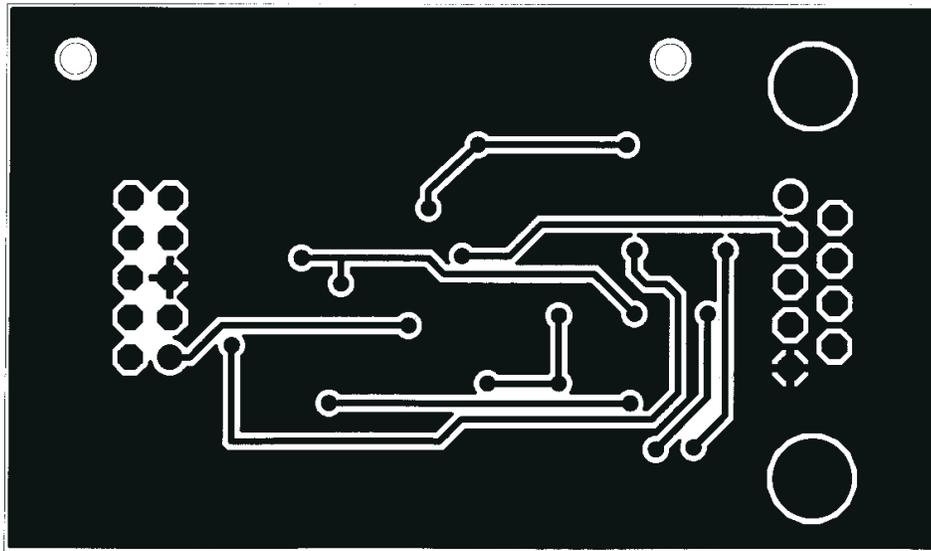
通用 BSL 接口 PCB 布局，底视图
